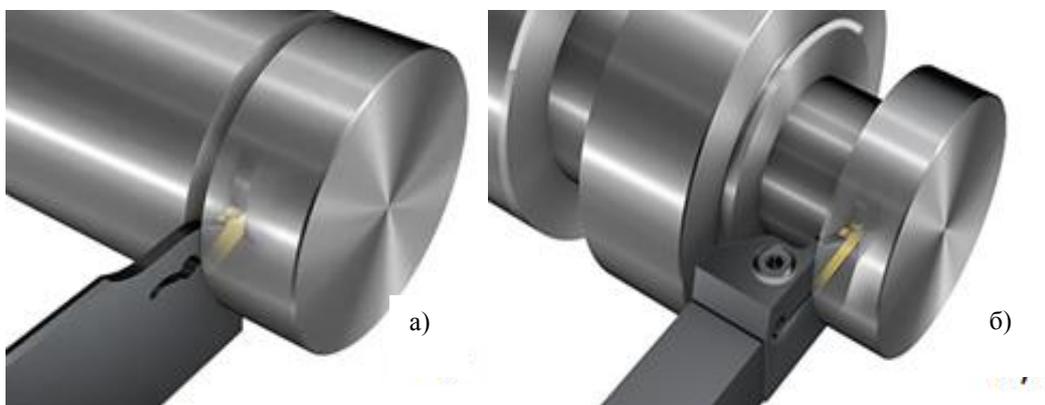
Крепление СТП: а – пружинящие свойства корпуса; б – крепление винтом [1]
